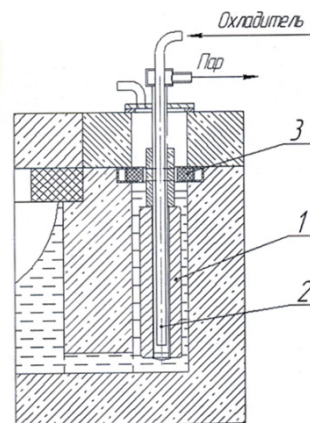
Схема процесса формирования полый слитка намораживанием на трубу-кристаллизатор
